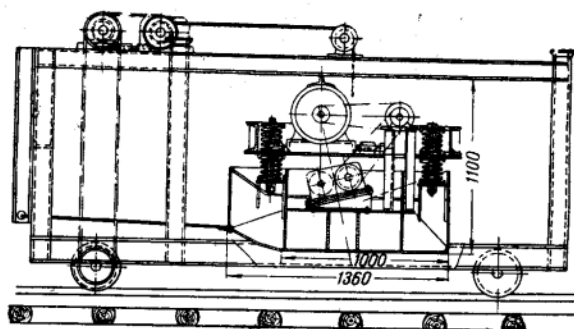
Схема установки для формования скорлуп сборных железобетонных оболочек
